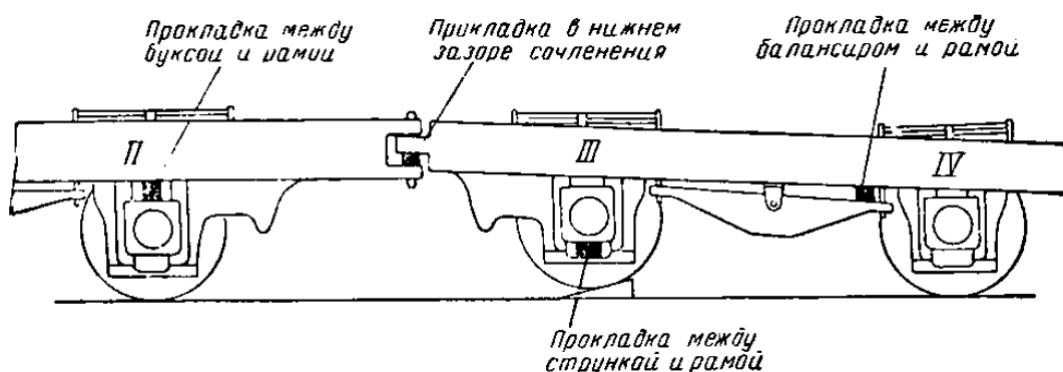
Расположение приспособлений при вывешивании третьей колесной пары
